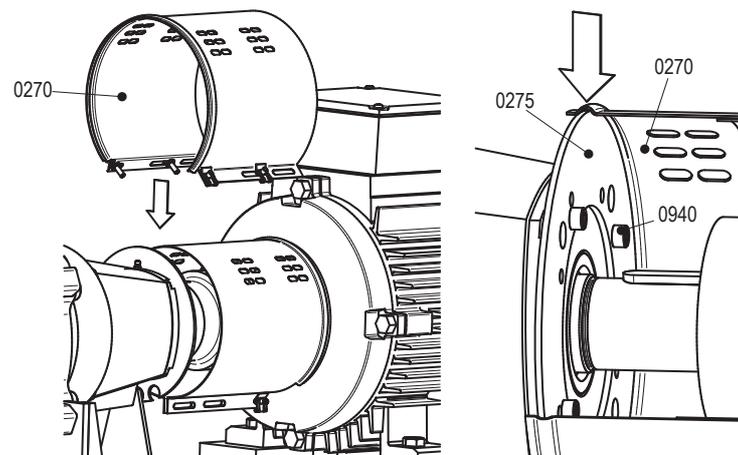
Montieren der Haube auf der Pumpenseite.
